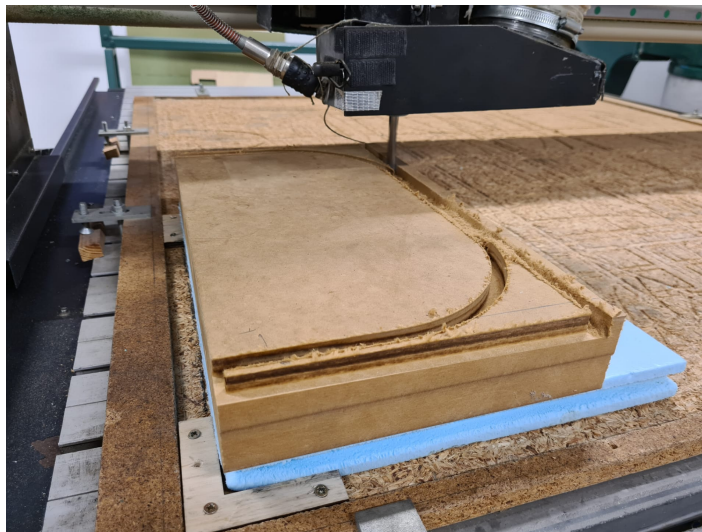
Desbaste do molde para a perna traseira com fresa CNC.
